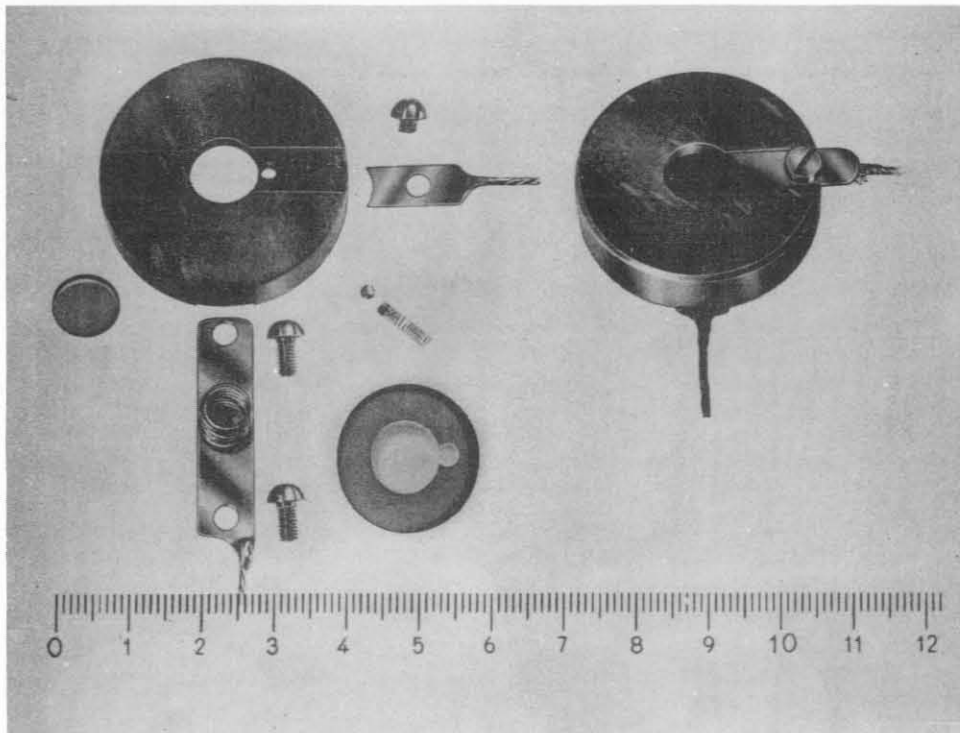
Componenti di un rivelatore da utilizzare come integrle prima e dopo il montaggio.
